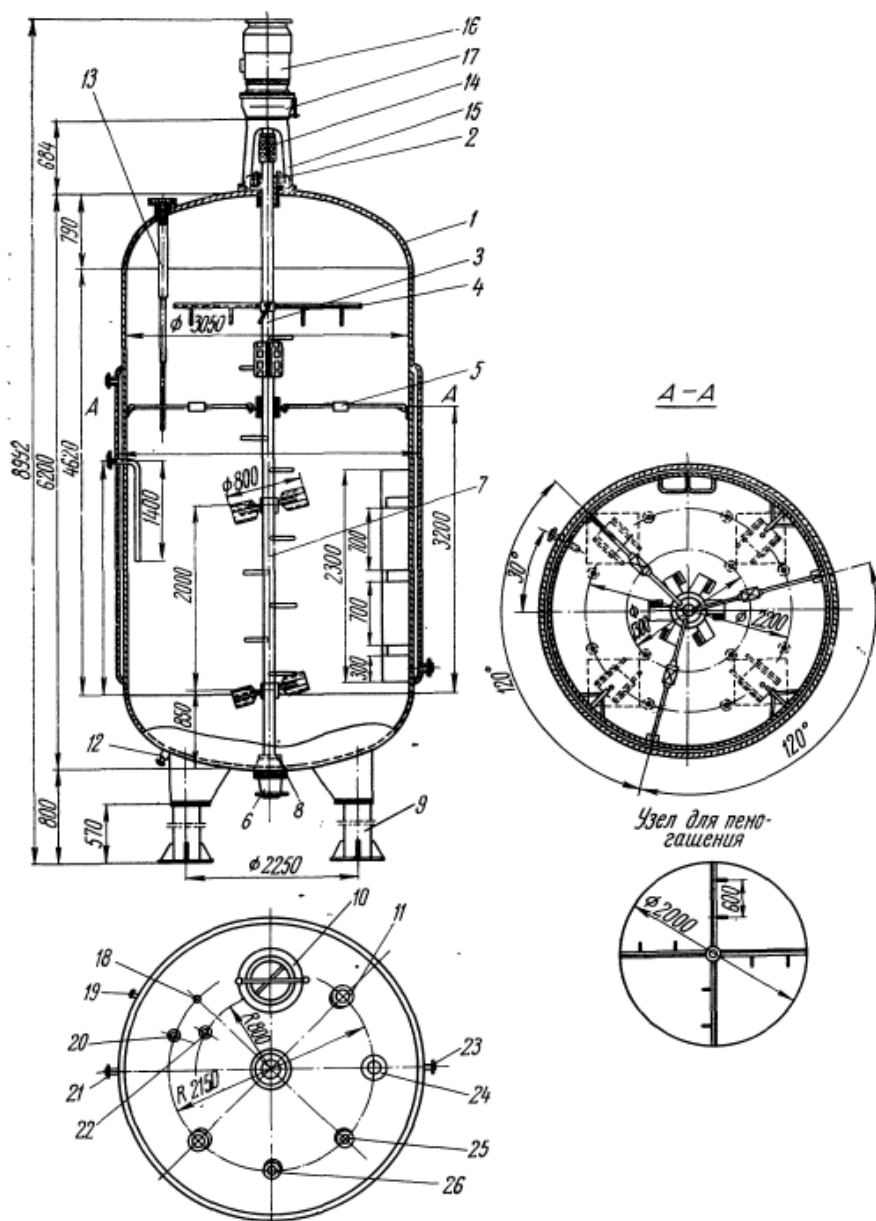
а. Ферментатор конструкции КБ ВНИИФСа с механической мешалкой и подводом воздуха через форсунки:
